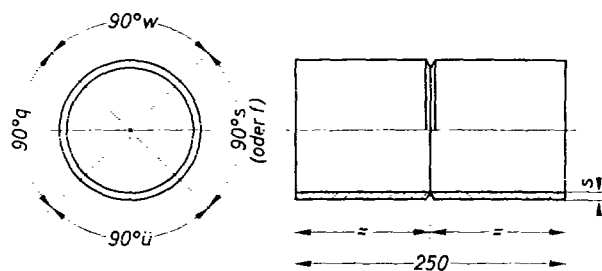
Stumpfnahmprüfstück für Rohrschweißer in Schweißposition w, s, ü, q
